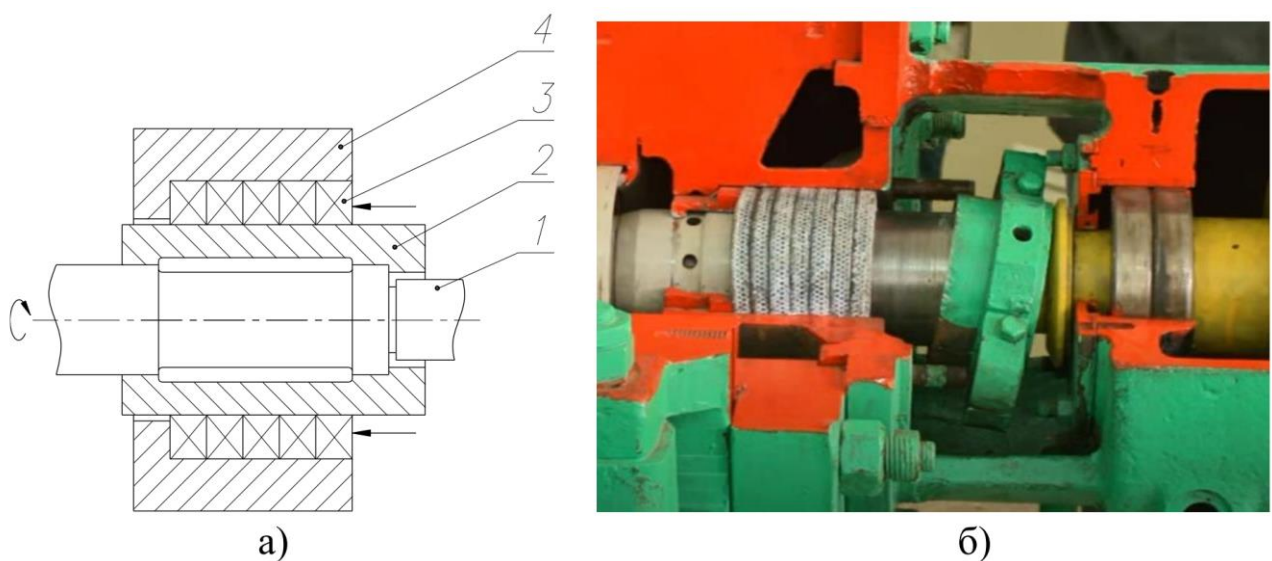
Схема роботи захисної втулки консольних насосів: а – принципова схема; б – загальний вигляд; 1 – вал; 2 – захисна втулка; 3 – сальникова набивка; 4 – корпус насоса [4, 7, 18].
